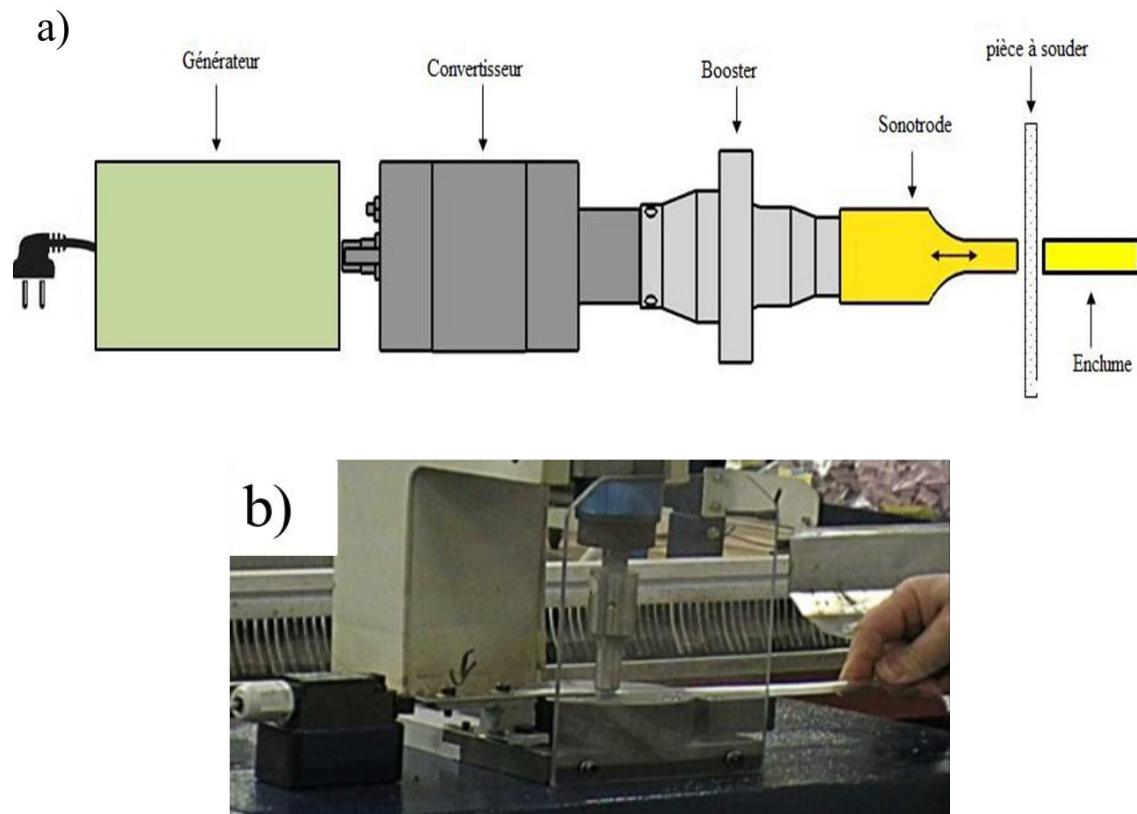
Soudage par ultrasons : a) schéma du procédé, b) machine de soudage[10].
